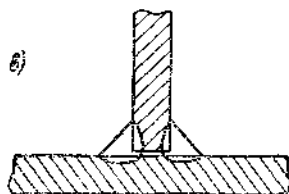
Схема расположения сварных швов в пространстве
